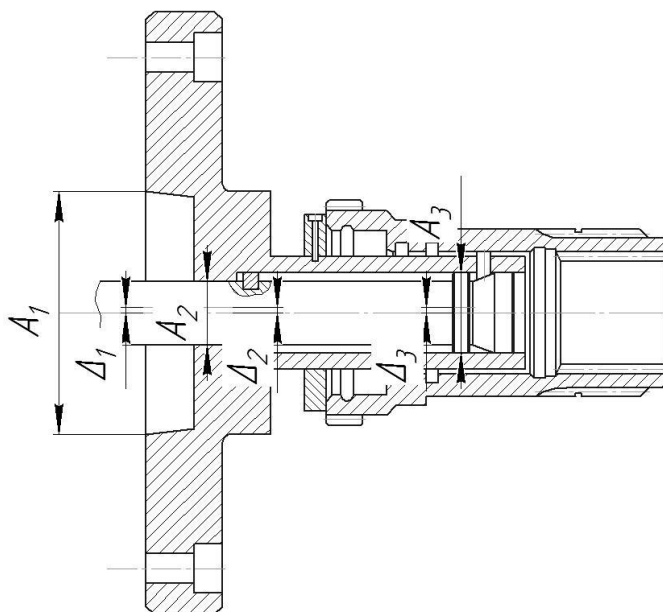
Расчетная схема погрешностей элементов приспособления
